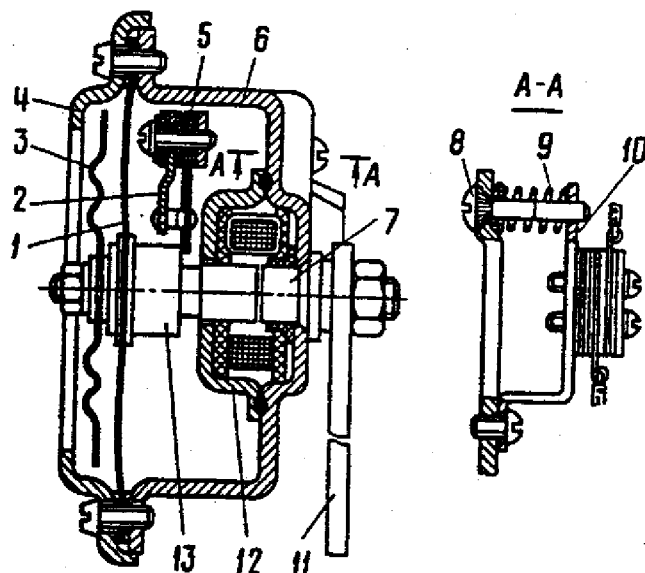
Buzina: 1 - membrana; 2 - retentor do contato fixo; 3 - difusor; 4 - tampa; 5 - placa de contato móvel; 6 - carcaça; 7 - núcleo; 8 - parafuso de ajuste; 9 - mola do parafuso de ajuste; 10 - ponte de contato; 11 - suporte de fixação da buzina; 12 - armadura do induzido; 13 - induzido.
